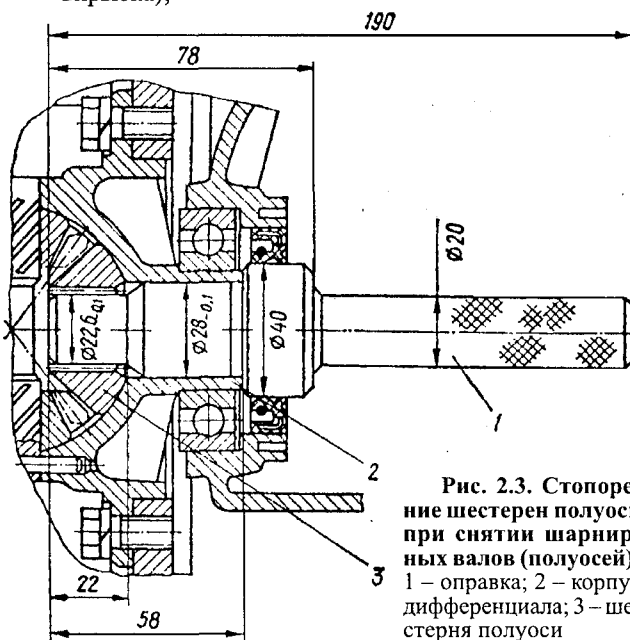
Стопорные шестерни полуоси при снятии шарнирных валов (полуосей): 1 – оправка; 2 – корпус дифференциала; 3 – шестерня полуоси
